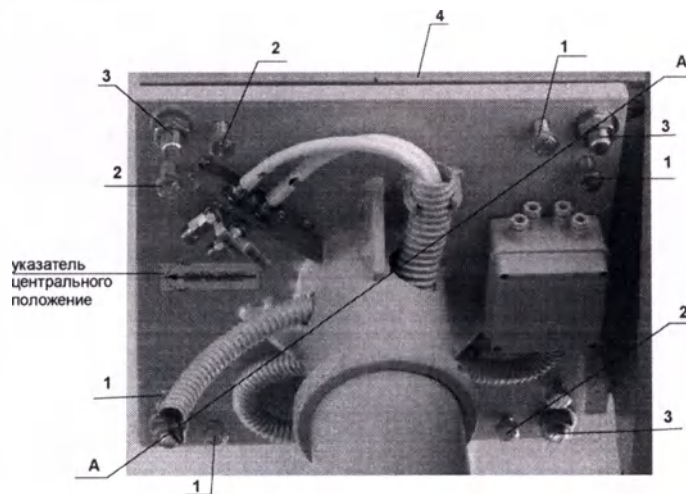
Расположение наклейки “центральное положение”, регулировочных болтов и гаек крепления основания консоли (типовой вид)
